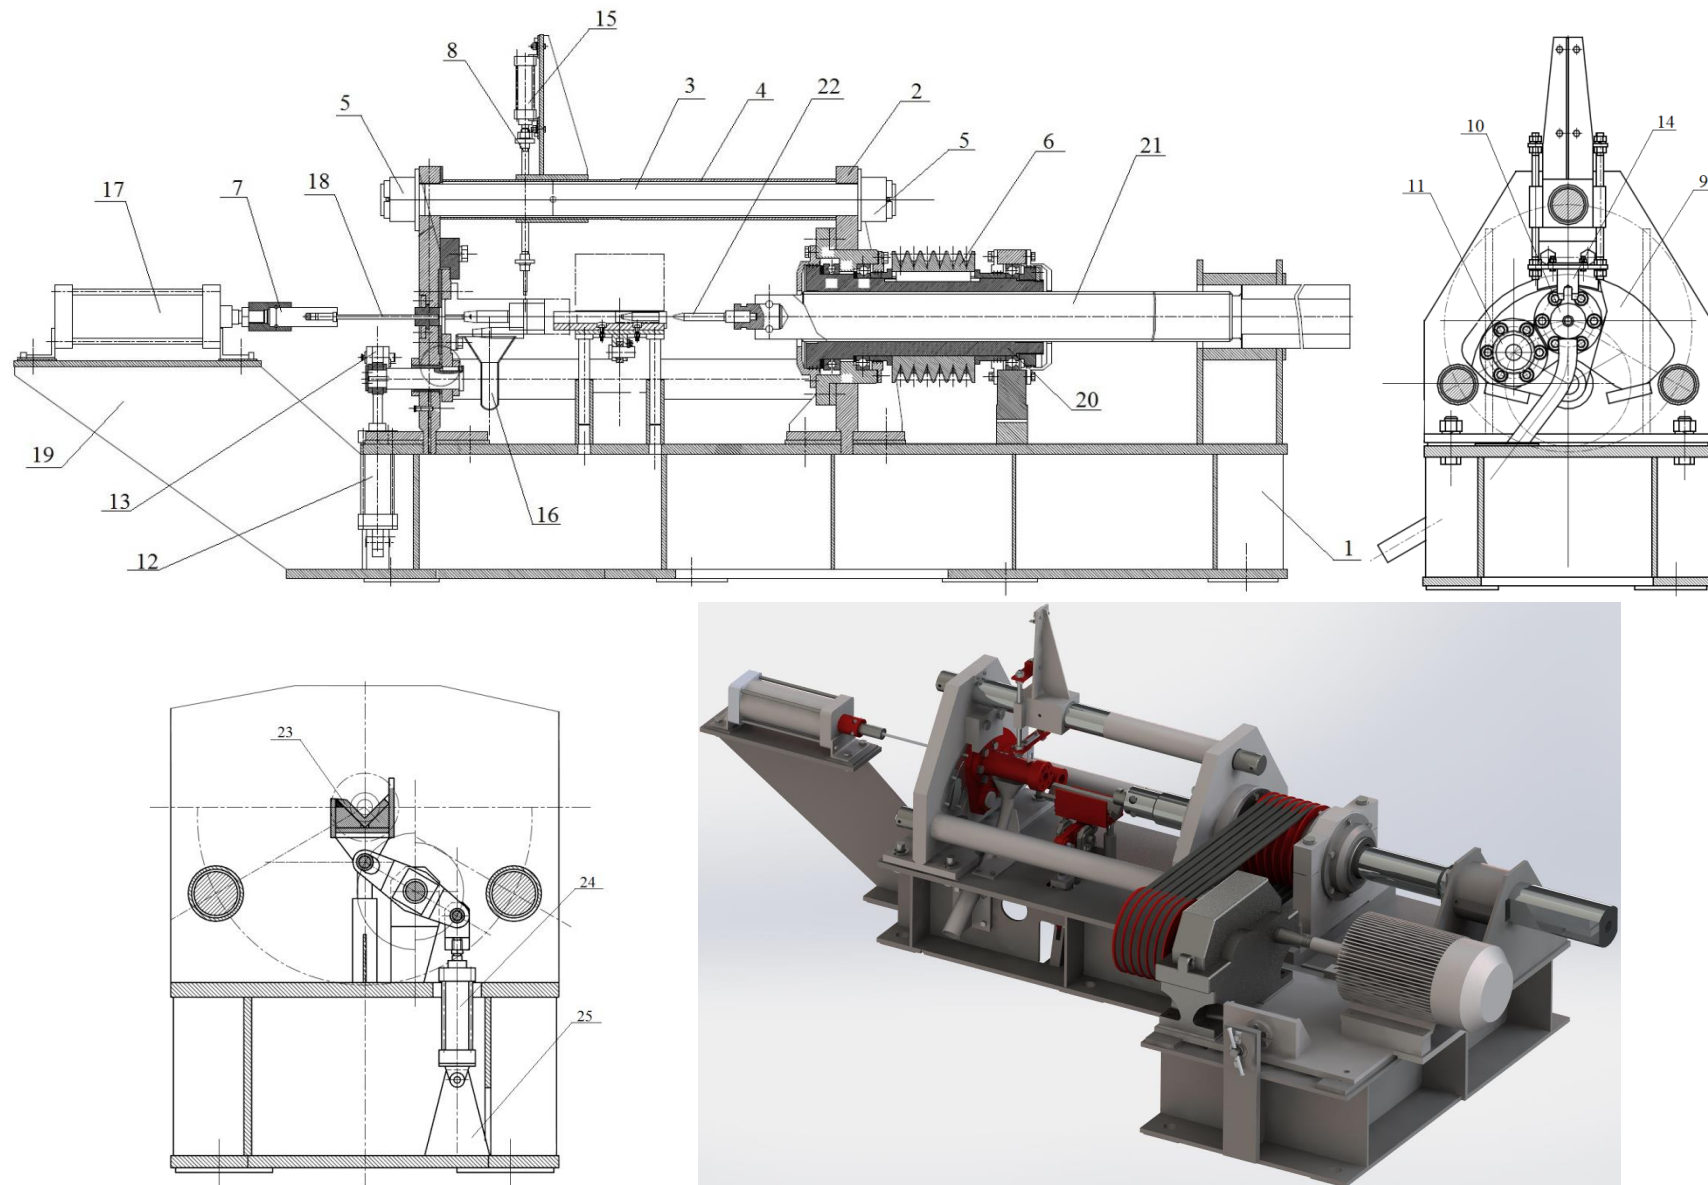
Пресс калибровочный с электромеханическим приводом
